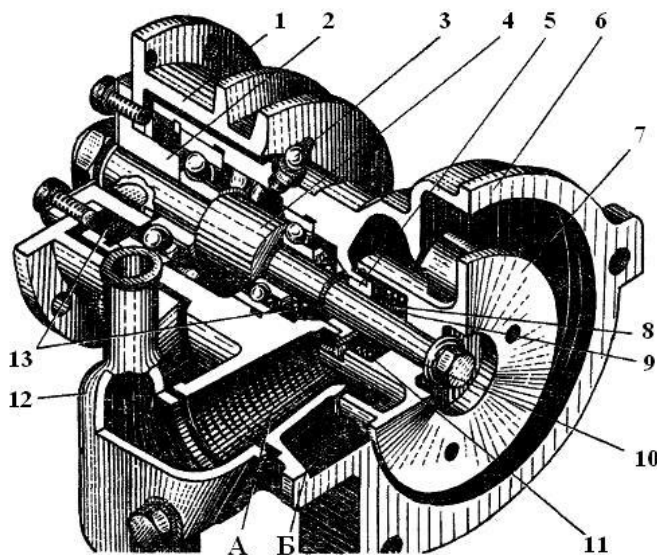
Водяной насос системы охлаждения тракторов: 1 – шкив; 2 – ступица шкива; 3 – масленка; 4 – валик; 5 – втулка корпуса; 6 – корпус; 7 – крыльчатка; 8 – обойма сальника; 9 – манжета сальника; 10 – уплотняющая шайба; 11 – упорная пружина сальника; 12 – патрубок; 13 – самоподжимные каркасные сальники; А – полость всасывания; Б – полость нагнетания
